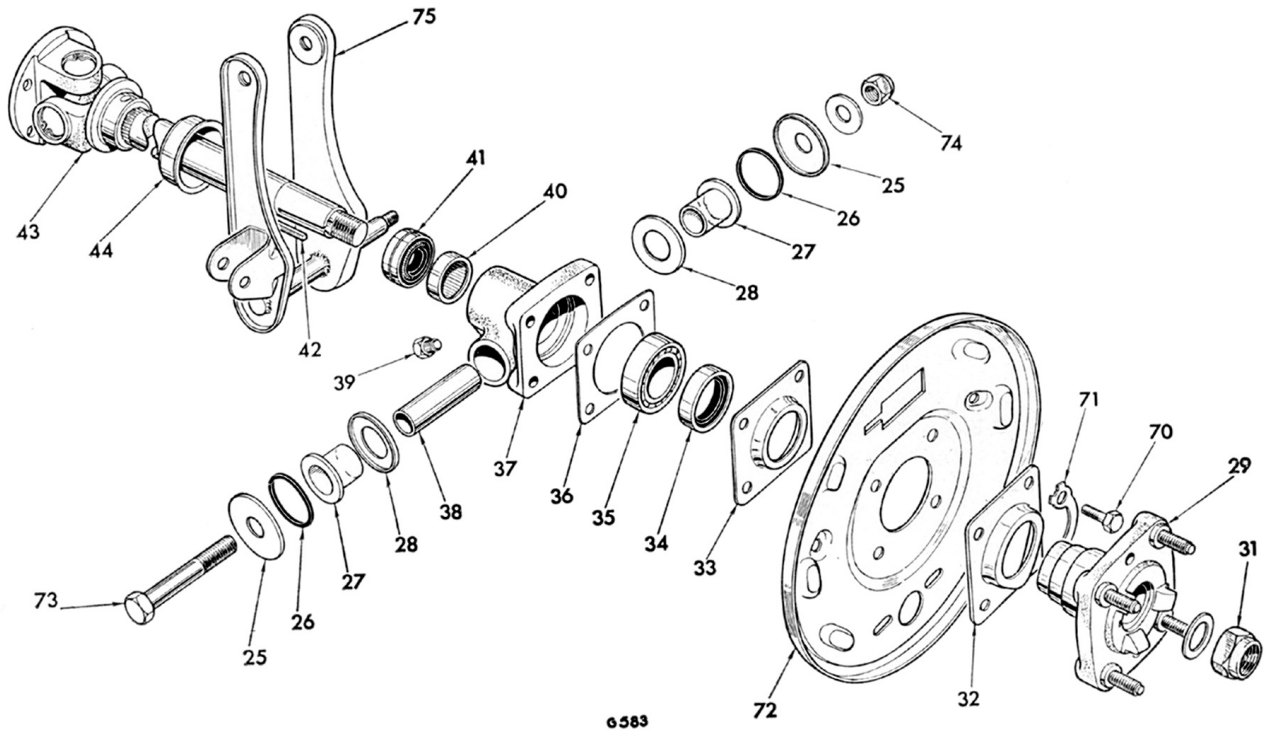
Détails du demi-arbre extérieur et du moyeu
